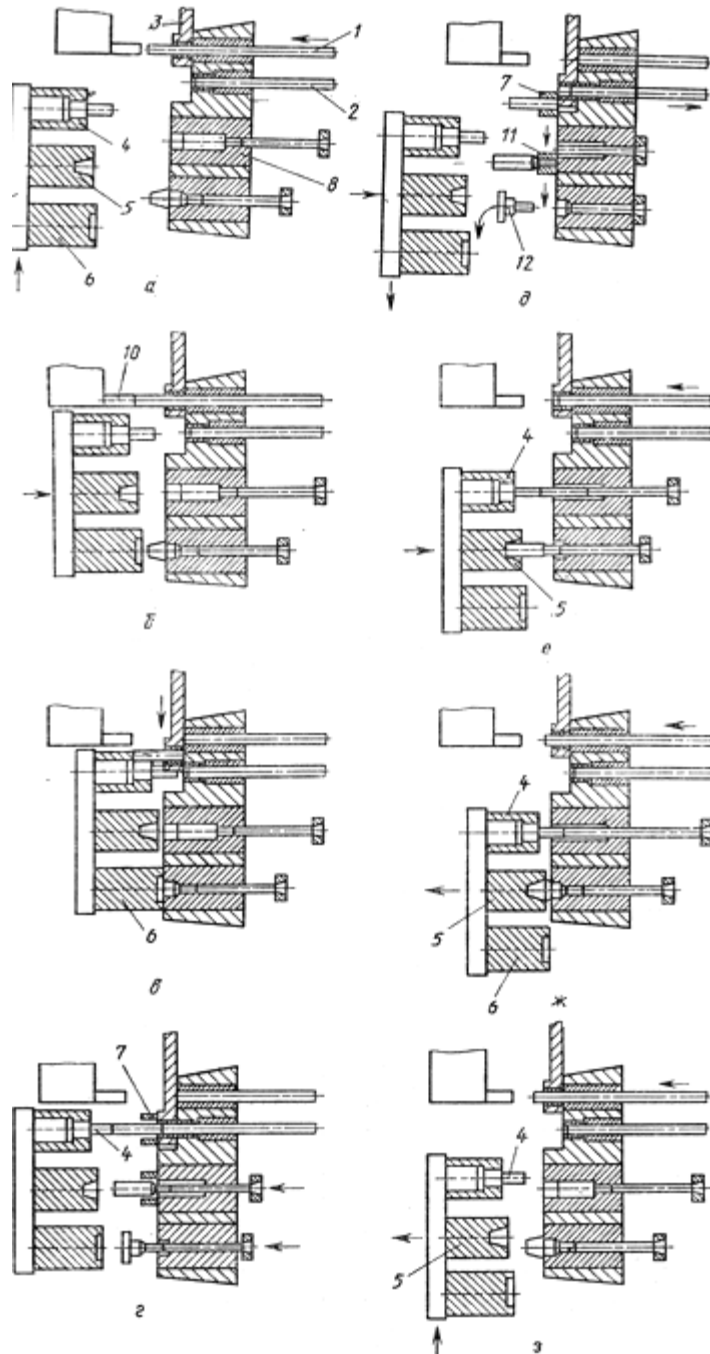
Штампування деталі на двопозиційному трьохударному пресі-автоматі:
